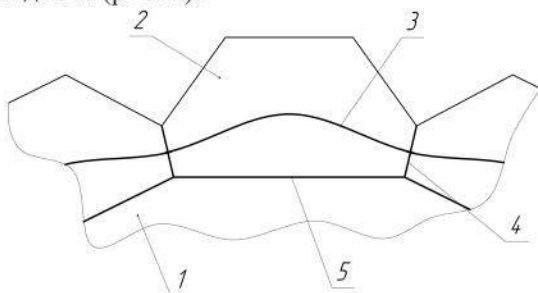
Схема зварювання зуба з остовом зношеного диска: 1 – фрагмент зношеного диска; 2 – зуб; 3 – лінія зварювання диска з остовом зношеного диска з неробочої сторони; 4 – лінія зварювання зубів між собою; 5 – лінія зварювання зуба з остовом зношеного диска з робочої сторони
